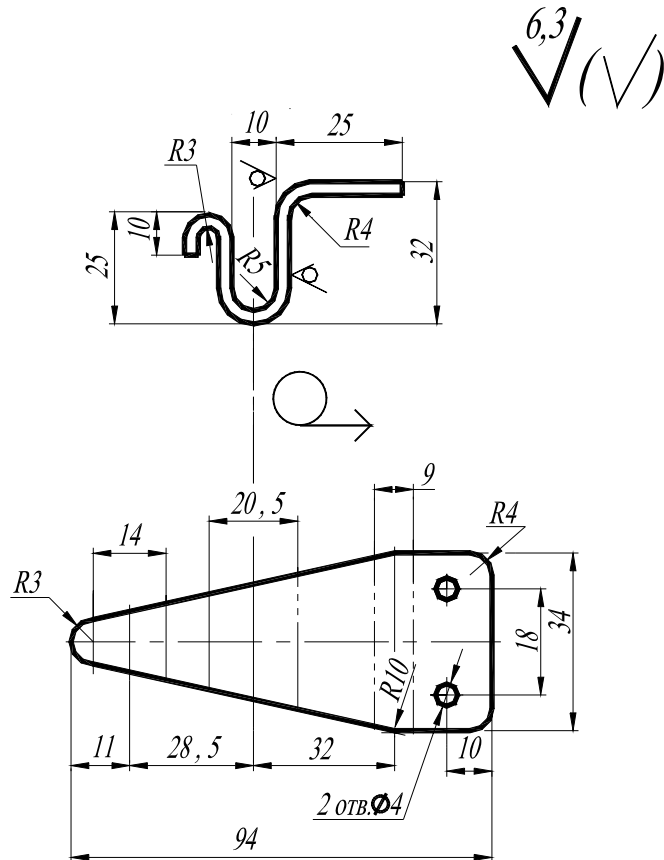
Нанесение размеров детали, изготовленной гибкой
